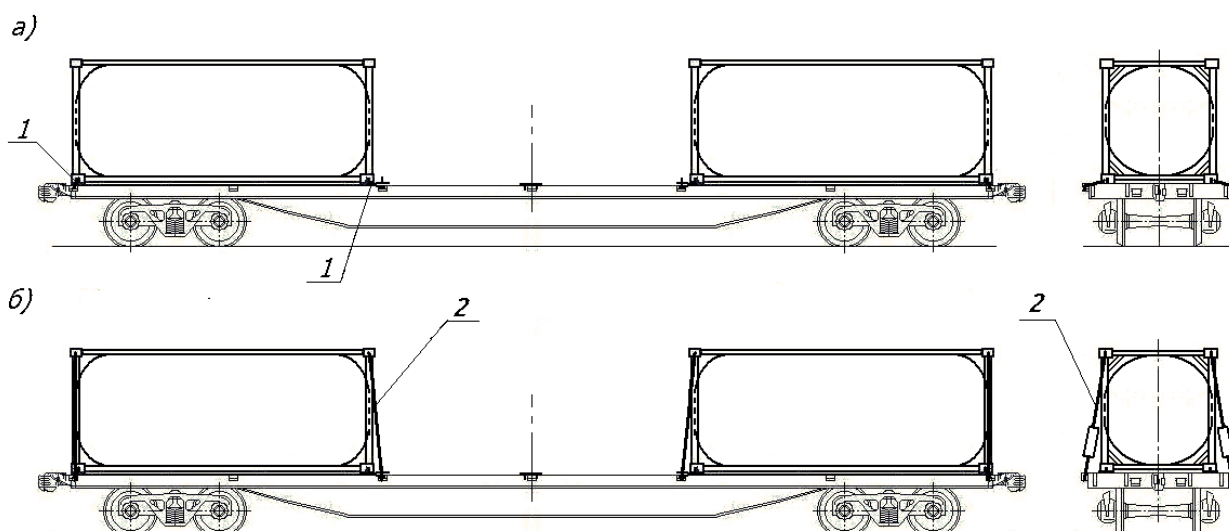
Дополнительное крепление контейнеро-цистерн на платформе для крупнотоннажных контейнеров:
